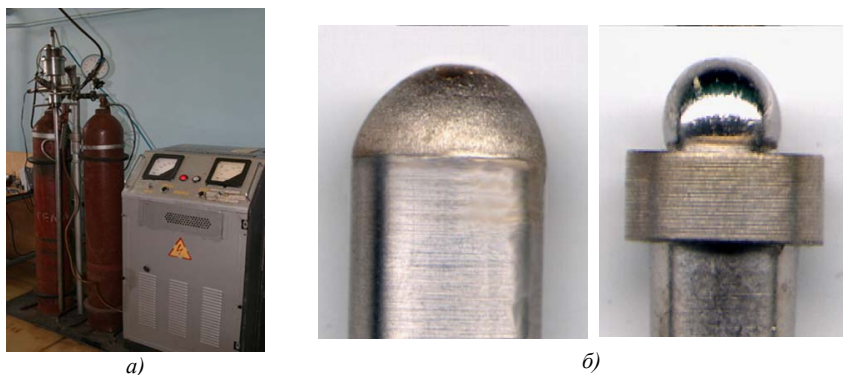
Установка сварки в контролируемой атмосфере УСК-1 (а) и образцы сварных соединений (б)
